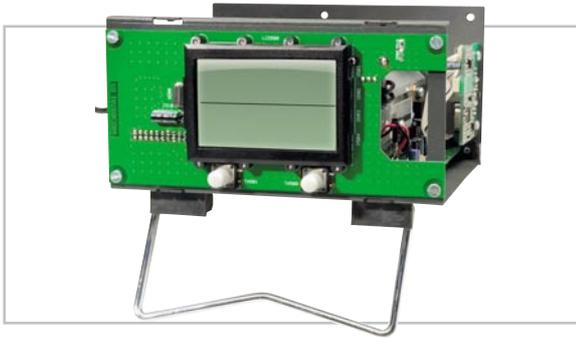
Montage der Frontplatte am Gehäuseunterteil
